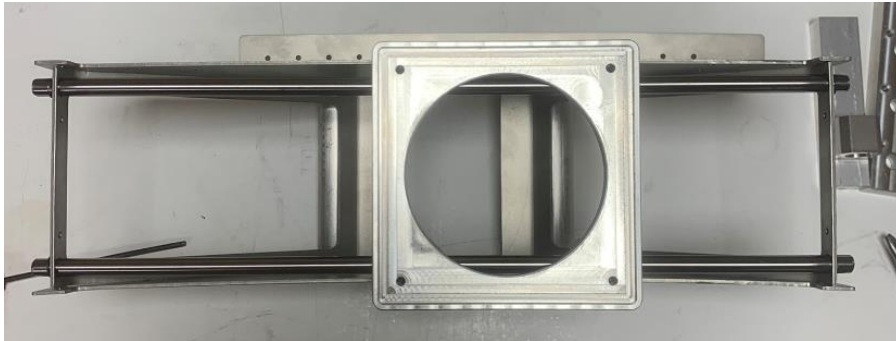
21: Düz millerin tabla taşıyıcıya montajı
